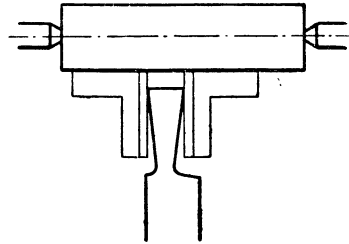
Отрезной твердосплавный резец конструкции токаря-скоростника т. Мехонцева.
